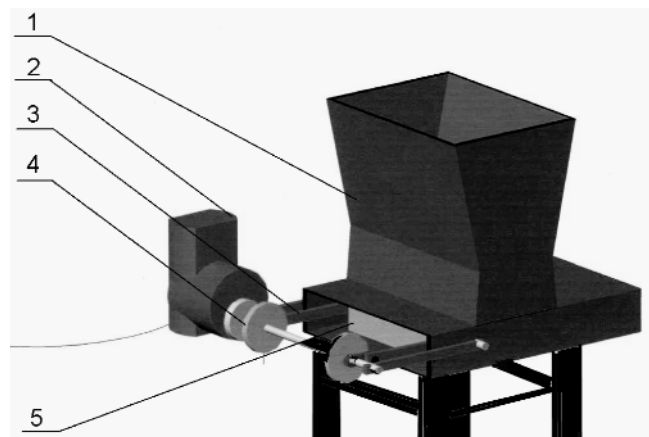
Специальная установка для устройства подливки под оборудование с высоким фундаментом :
